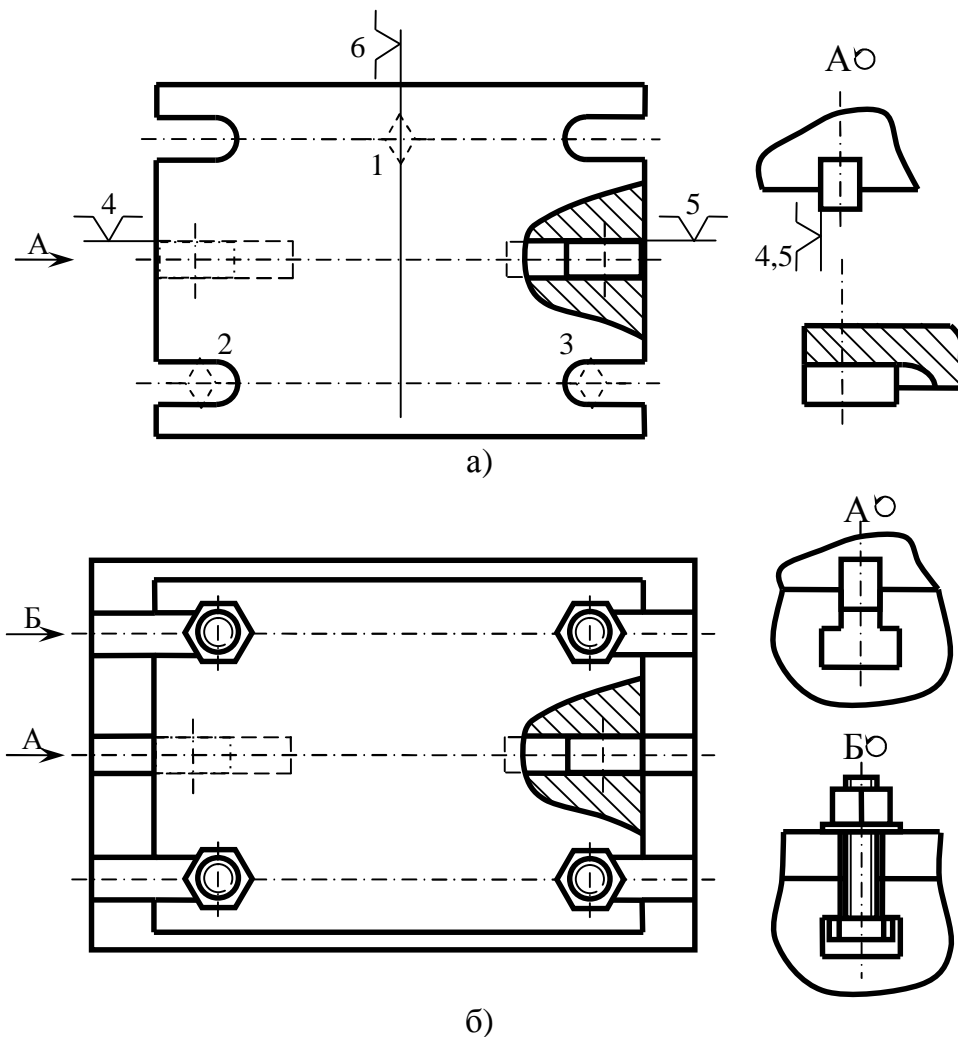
Установка приспособления на столе станка: схема базирования приспособления (а) и схема его установки (б)
